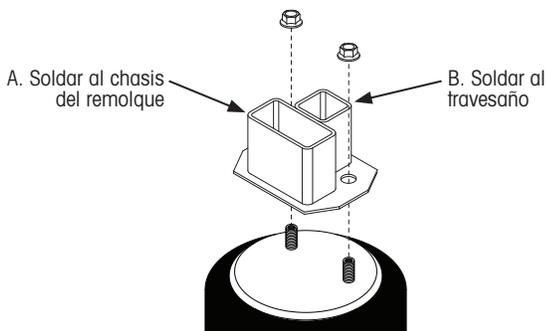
Placa de montaje soldable de cámara de aire, vista ISO.
